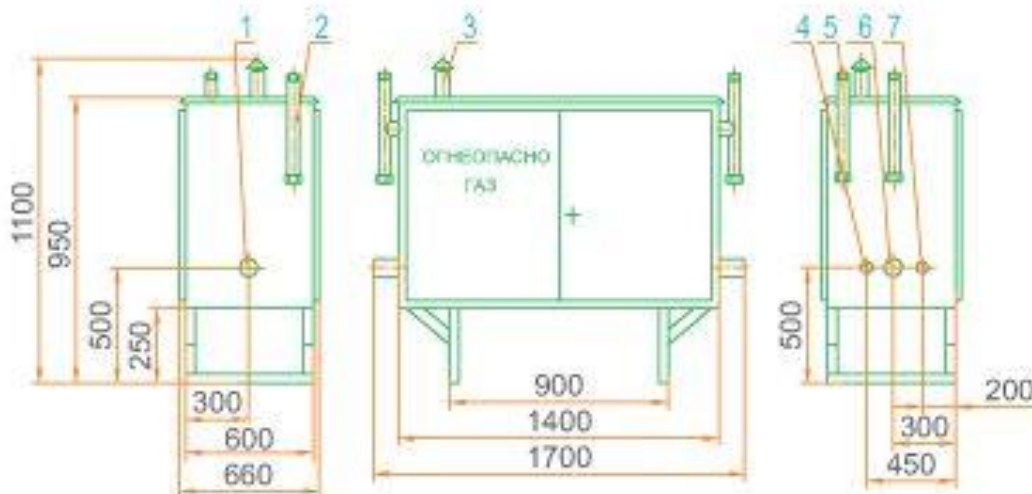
Габаритный чертёж ГРПШ-07-1
